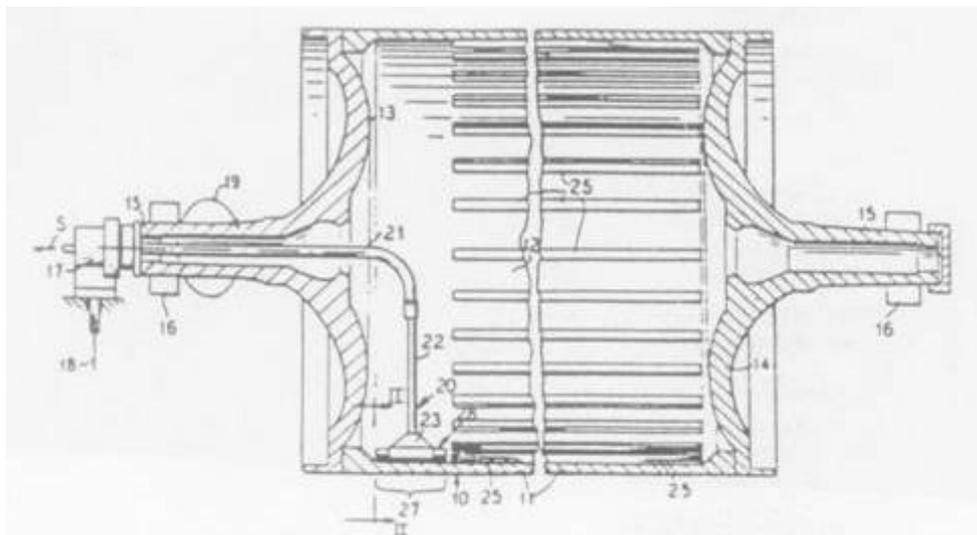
(FONTE: Yankee Dryers – W.G. Corboy, Jr.)
